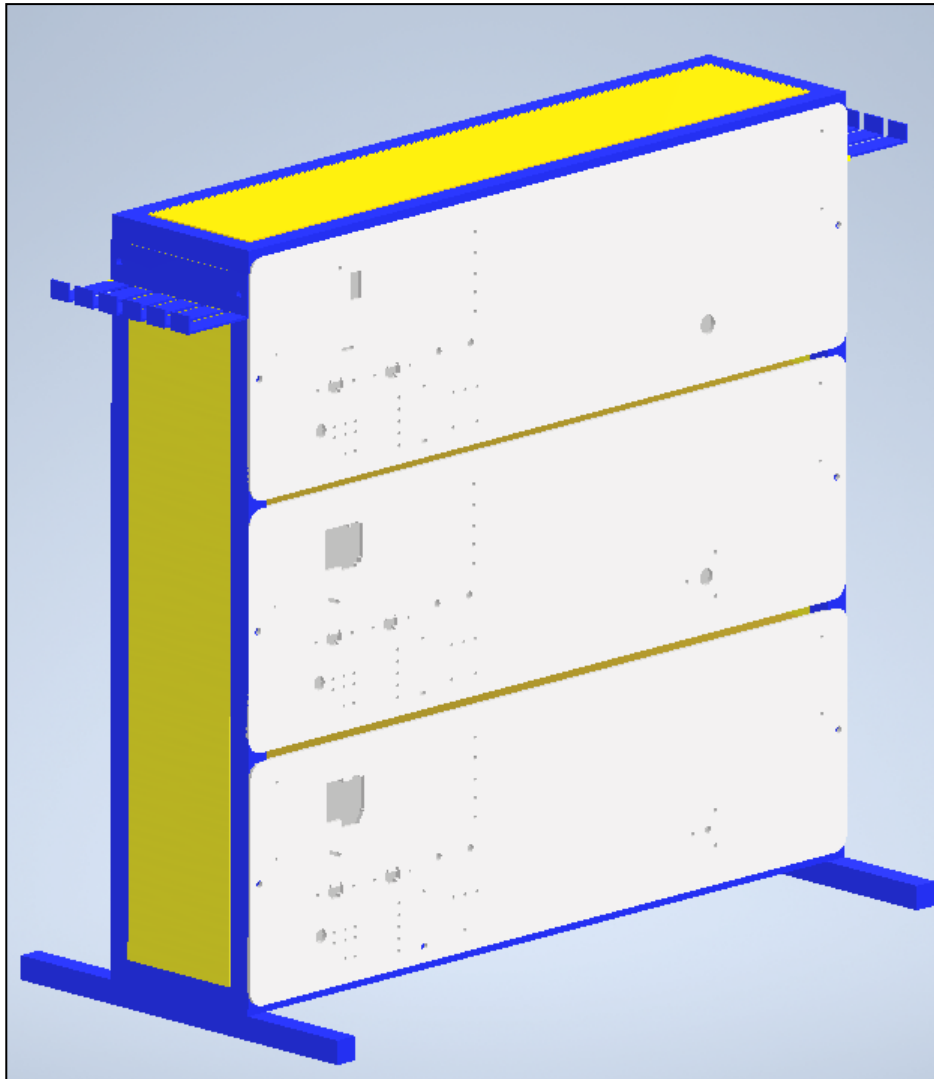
Diseño CAD del módulo del sistema de componentes auxiliares.
